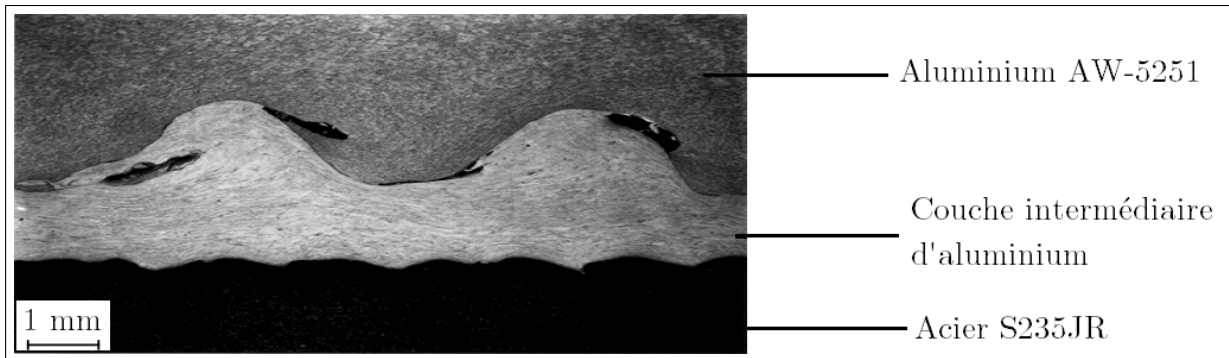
Observation macroscopique d'une structure hétérogène assemblée en soudage par explosion : mise en évidence de l'interface de soudage en vague [45].
